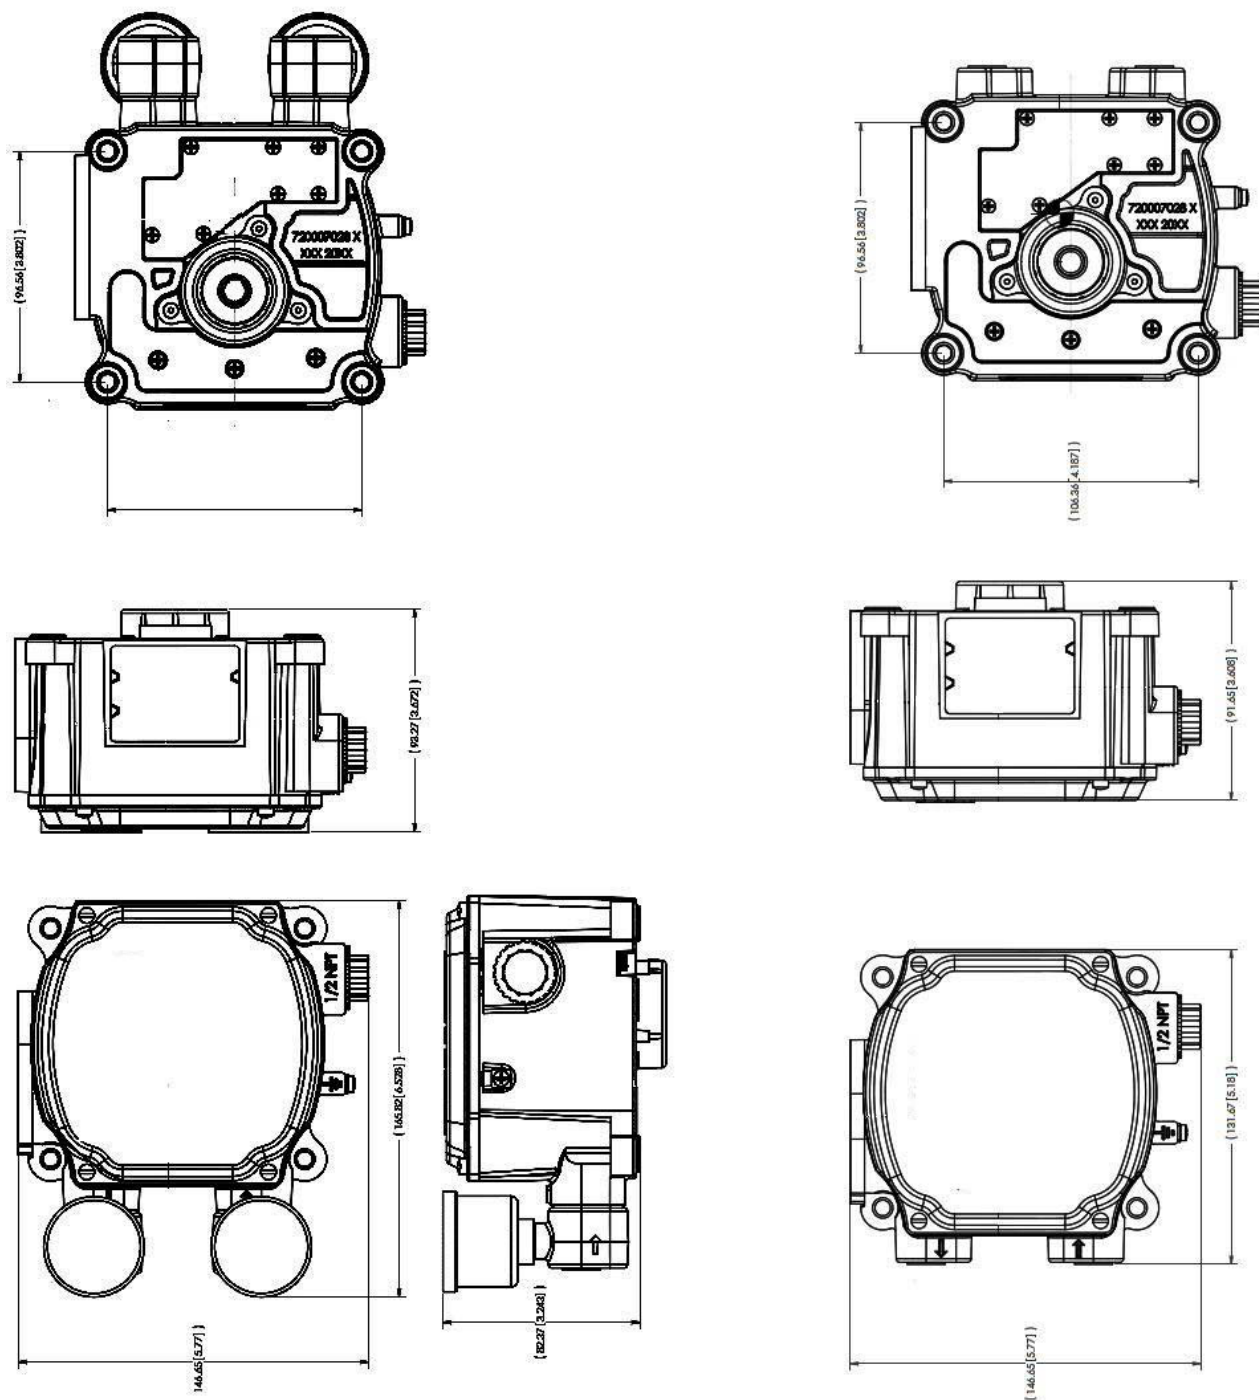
Dimensioni SVi1000 con e senza indicatori
